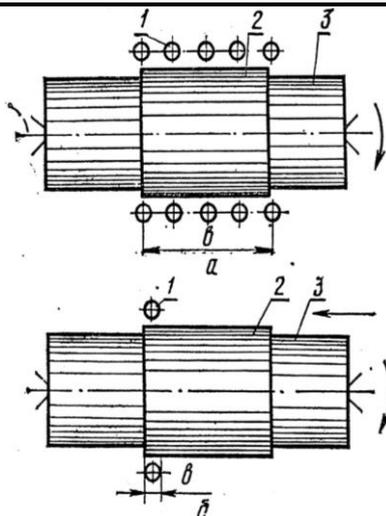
Схема способов наплавки током высокой частоты наружных цилиндрических поверхностей
